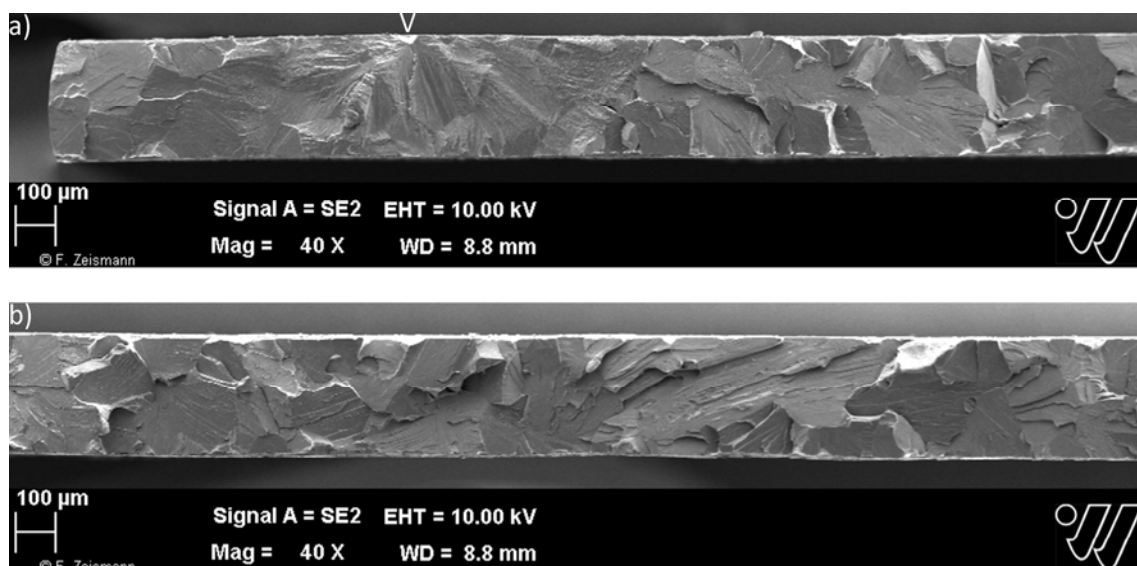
Übersicht einer typischen Bruchfläche bei Elektroblech, a) Stelle der Rissinitiierung und Bereich des Ermüdungsrisswachstums (siehe Markierung) und b) Restbruchfläche
